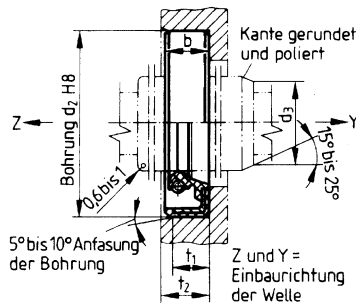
Einbau eines Wellendichtringes DIN 3760
